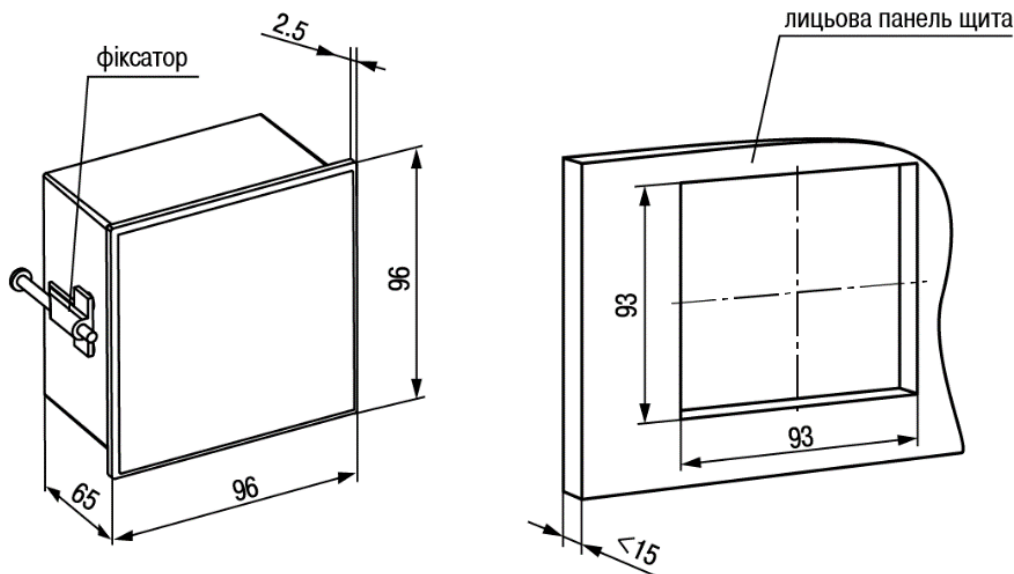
Габаритні розміри корпусу Щ1
